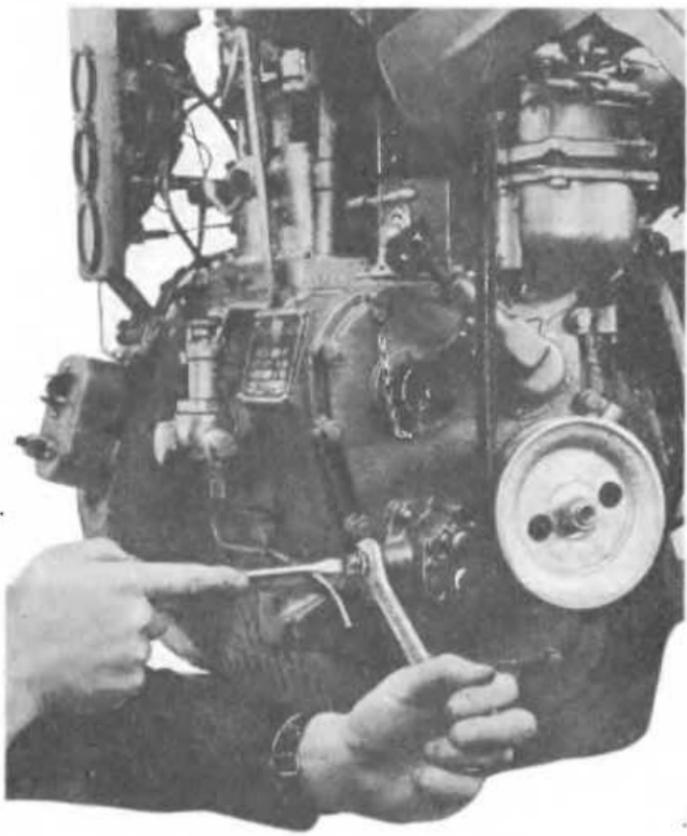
Регулировка давления масла на одно- и двухцилиндровых дизелях
